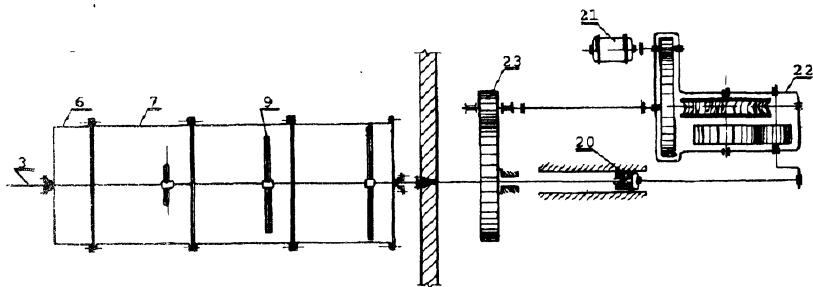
Горизонтальный непрерывнодействующий мешатель.
